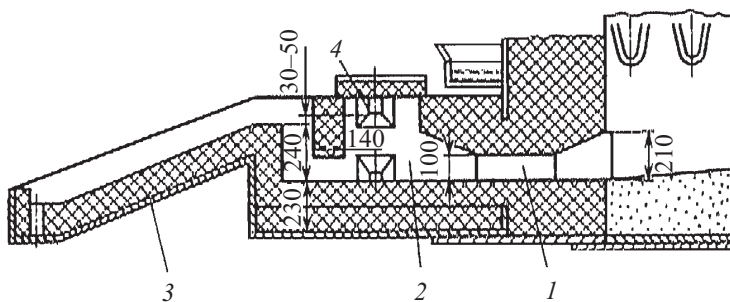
Устройство для непрерывного выпуска металла и скачивания шлака:
